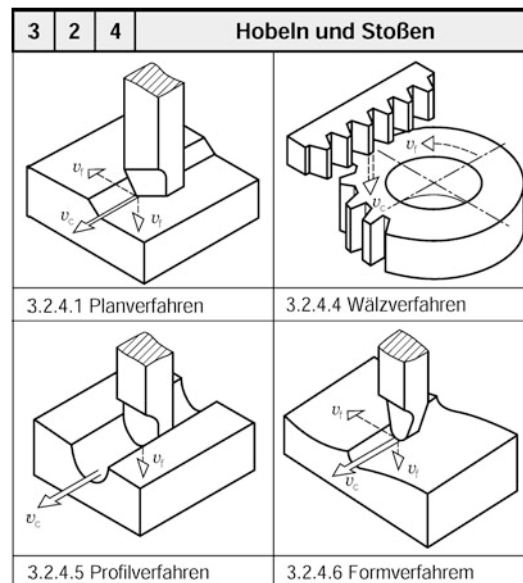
Plan-, Wälz-, Profil- und Formverfahren beim Hobeln und Stoßen / Rabotare plană, roți dințate, profilată [WES 10]
